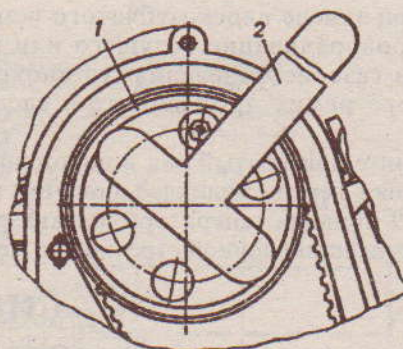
Проворачивание двигателя за шкив распределительного вала при регулировке зазоров в клапанном механизме: 1 - шкив распределительного вала; 2 - ключ М9811-321
